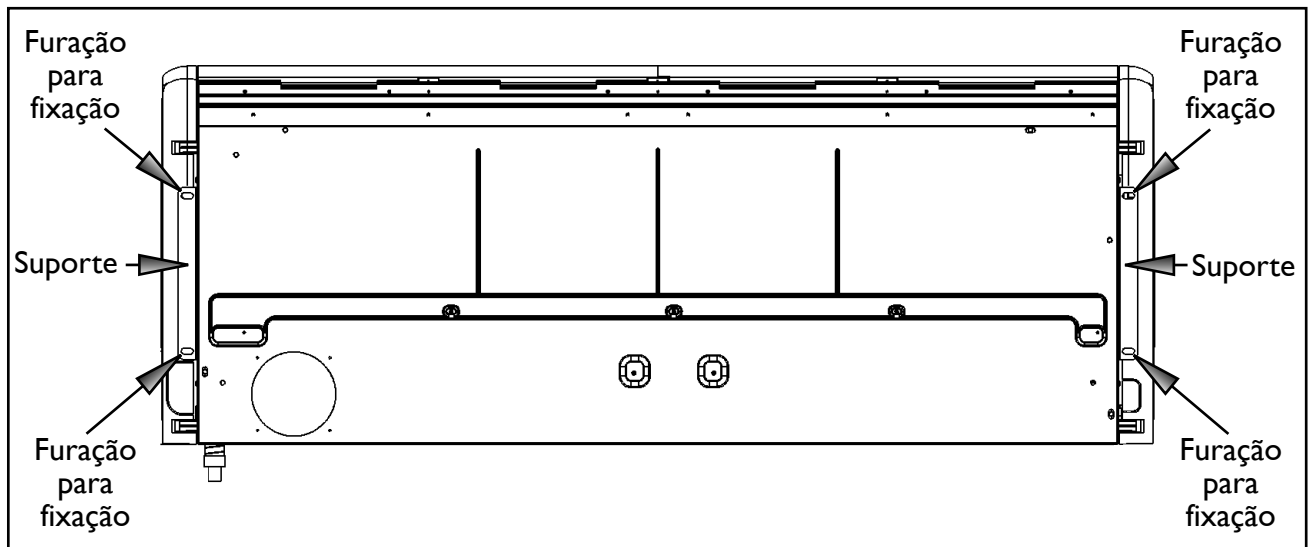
SUPORTES E FURAÇÃO PARA FIXAÇÃO
